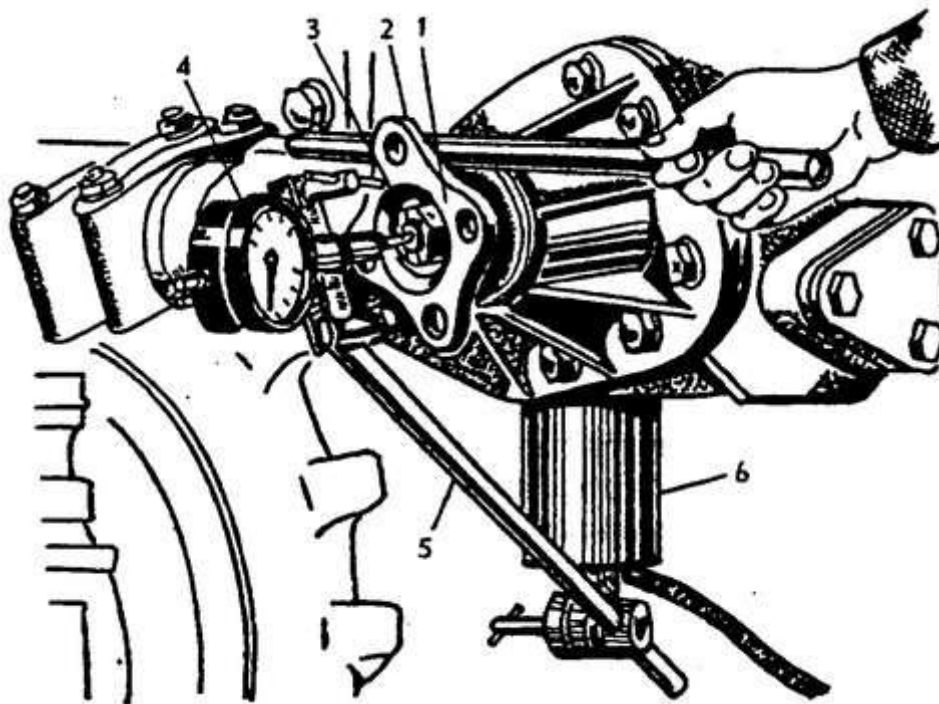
Измерение осевого зазора в подшипниках шестерни главной передачи переднего ведущего моста: 1 – фланец стакана ведущей шестерни; 2 – ломик; 3 – шток приспособления; 4 – индикатор; 5 – штатив; 6 – электромагнит
